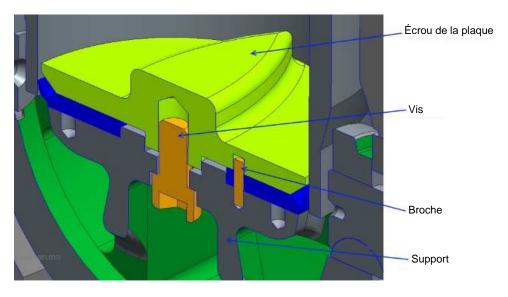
Installez la plaque de siège et l'écrou de la plaque de siège
